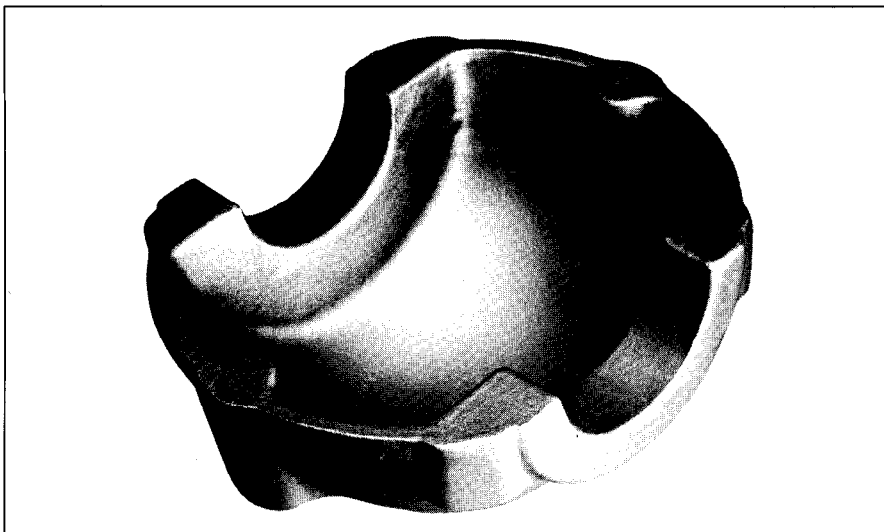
Schmiedeteile in einer Starrachse einer Baumaschine
